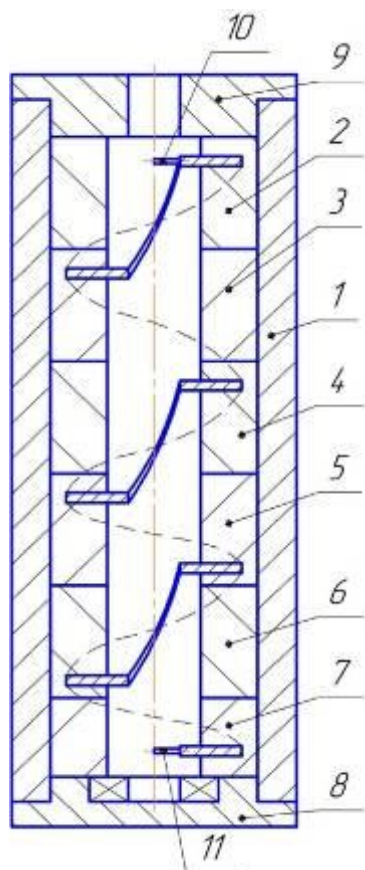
Схема форми із закладною ГЗ для виготовлення ШЗ (а)
